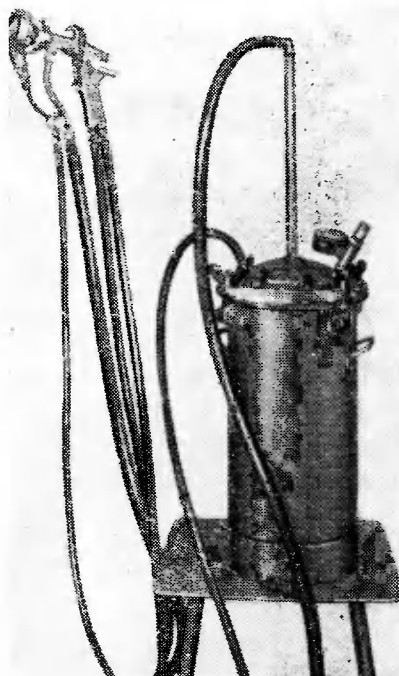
Установка WS-III (ГДР) для газопламенного напыления пластмасс
